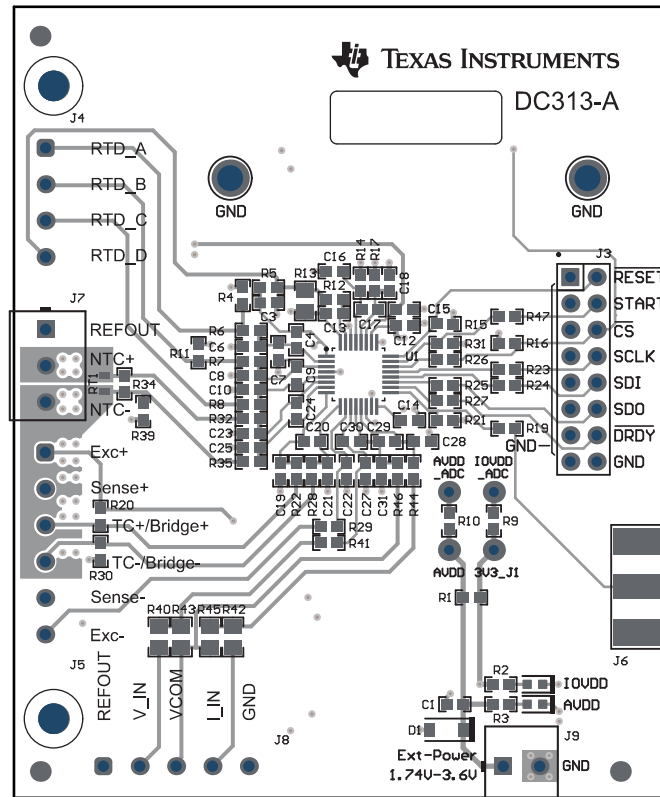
ADS124S18EVM PCB レイアウト — 上面層
